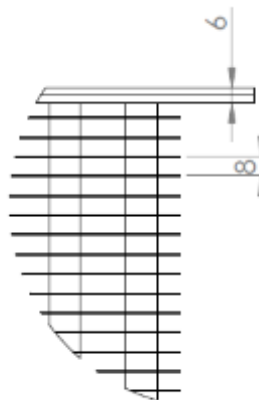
Dimensiones de la tubería de cobre del intercambiador
